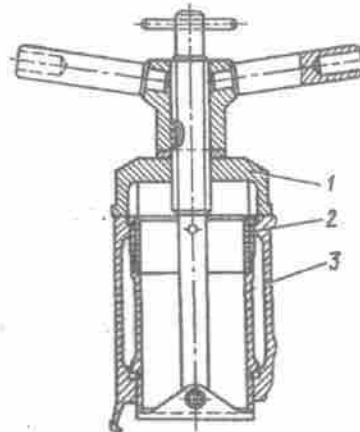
Abzieher zum Entfernen der Laufbuchsen des Zylinders:
